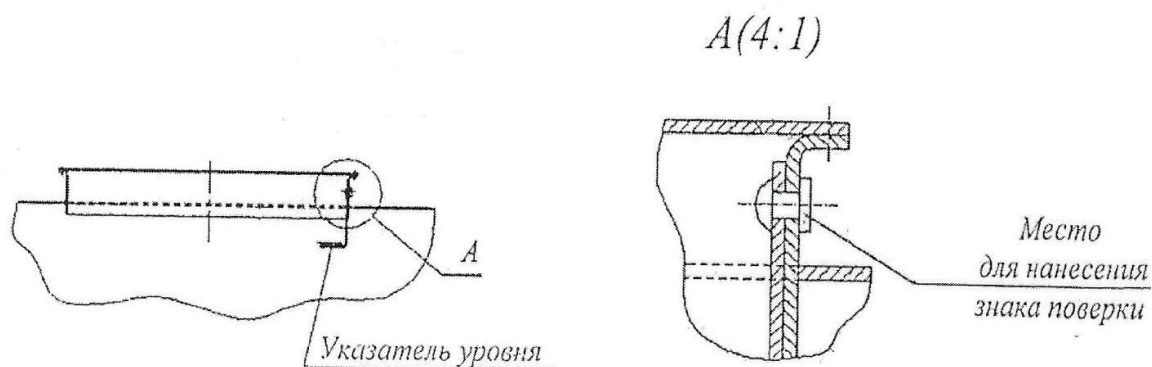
Схема пломбировки и обозначение места для нанесения знака поверки
